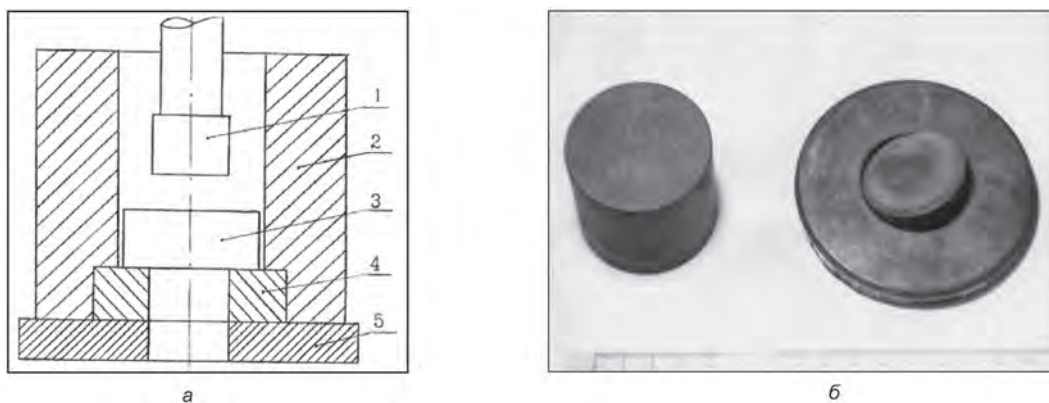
Получение изделий из чугуна типа шайб горячей пробивкой: а – схема процесса; б – исходная заготовка (слева) и чугунная шайба, полученная осадкой с последующей пробивкой (справа): 1 – пуансон; 2 – контейнер; 3 – исходная заготовка; 4 – матрица для пробивки; 5 – опора
